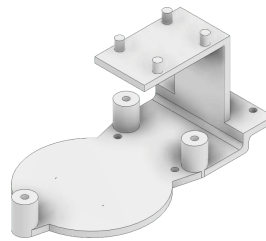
Vista isométrica del soporte para el montaje frontal del sensor FHL-LD20
